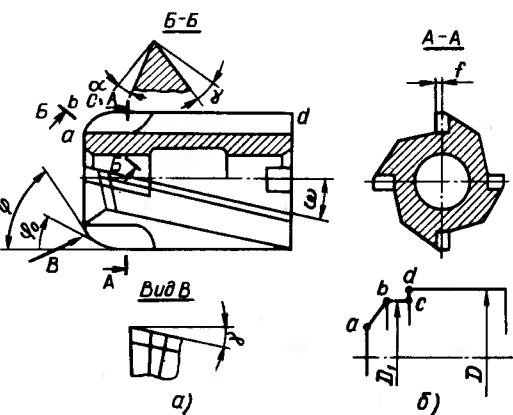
Геометрические параметры зенкера с твердосплавными пластинами
